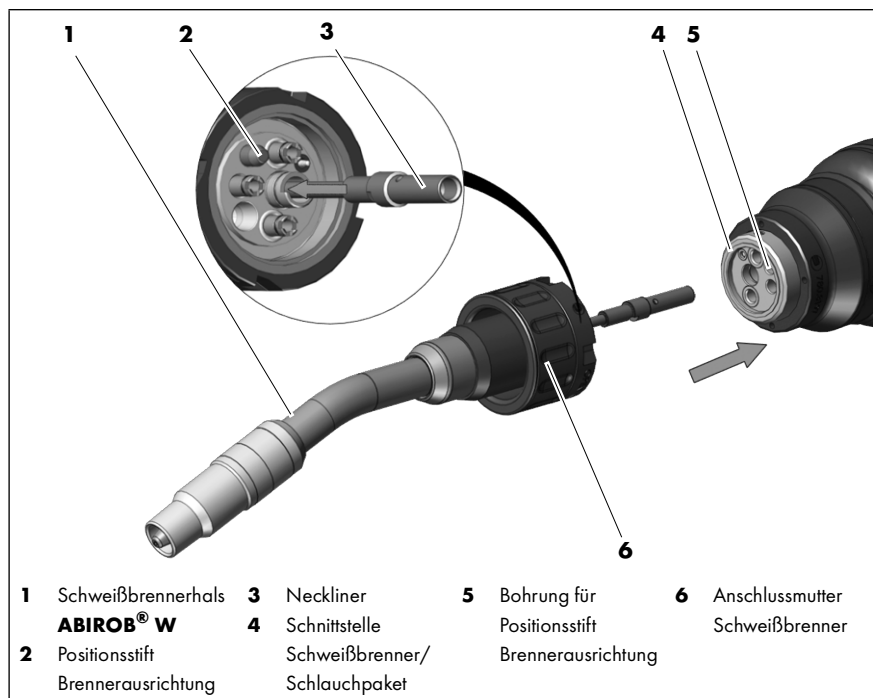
Schweißbrennerhals ABIROB® W befestigen (iCAT mini mit Wire-Brake)
